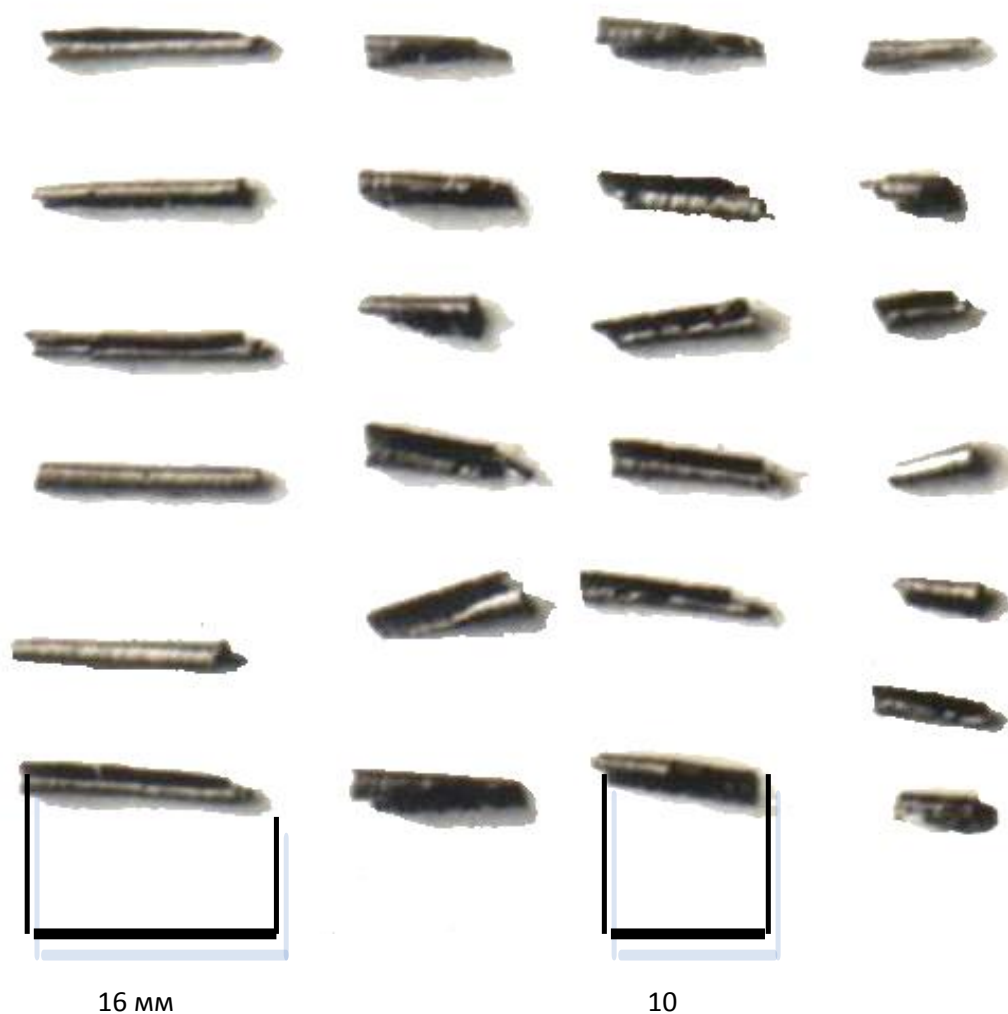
Стружки, зрізані чистовою твердосплавною фрезою $m = 20$ мм
